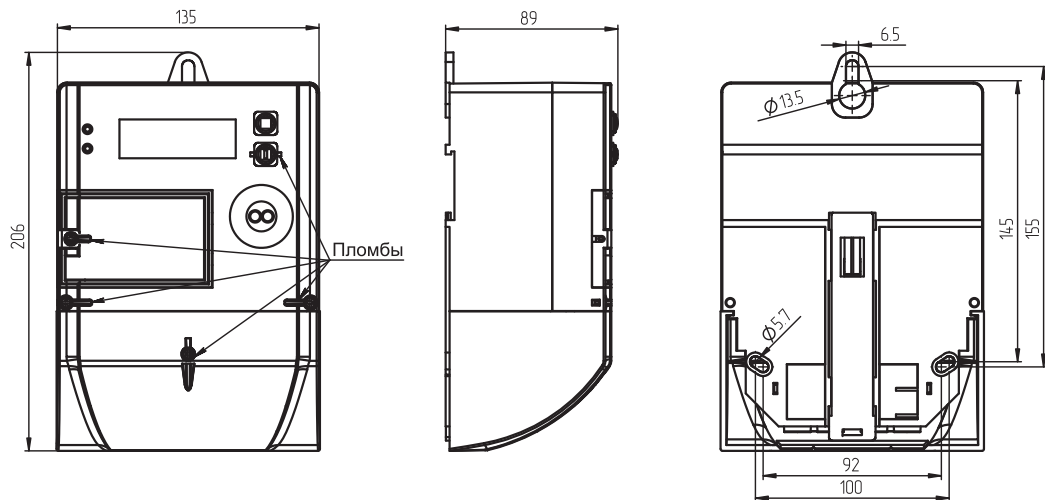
Общий вид, габаритные и установочные размеры, места установки пломб на корпусе однофазного счетчика типа MTX1
